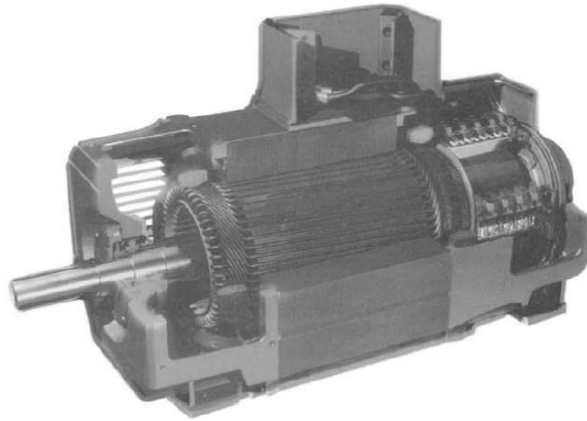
Vista de corte de un motor DC-Brushed Fuente: [44]
